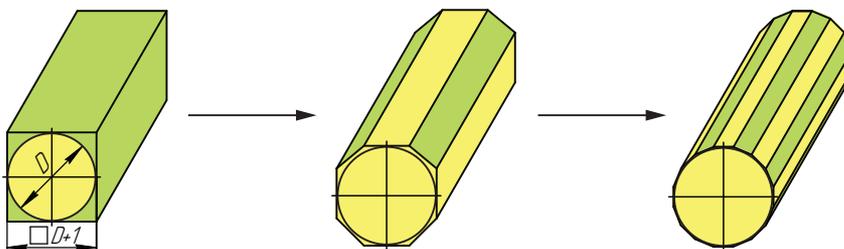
Последовательность изготовления деталей цилиндрической формы: выбор и разметка заготовки (слева), получение восьмигранника (в центре), получение шестнадцатигранника (справа)
